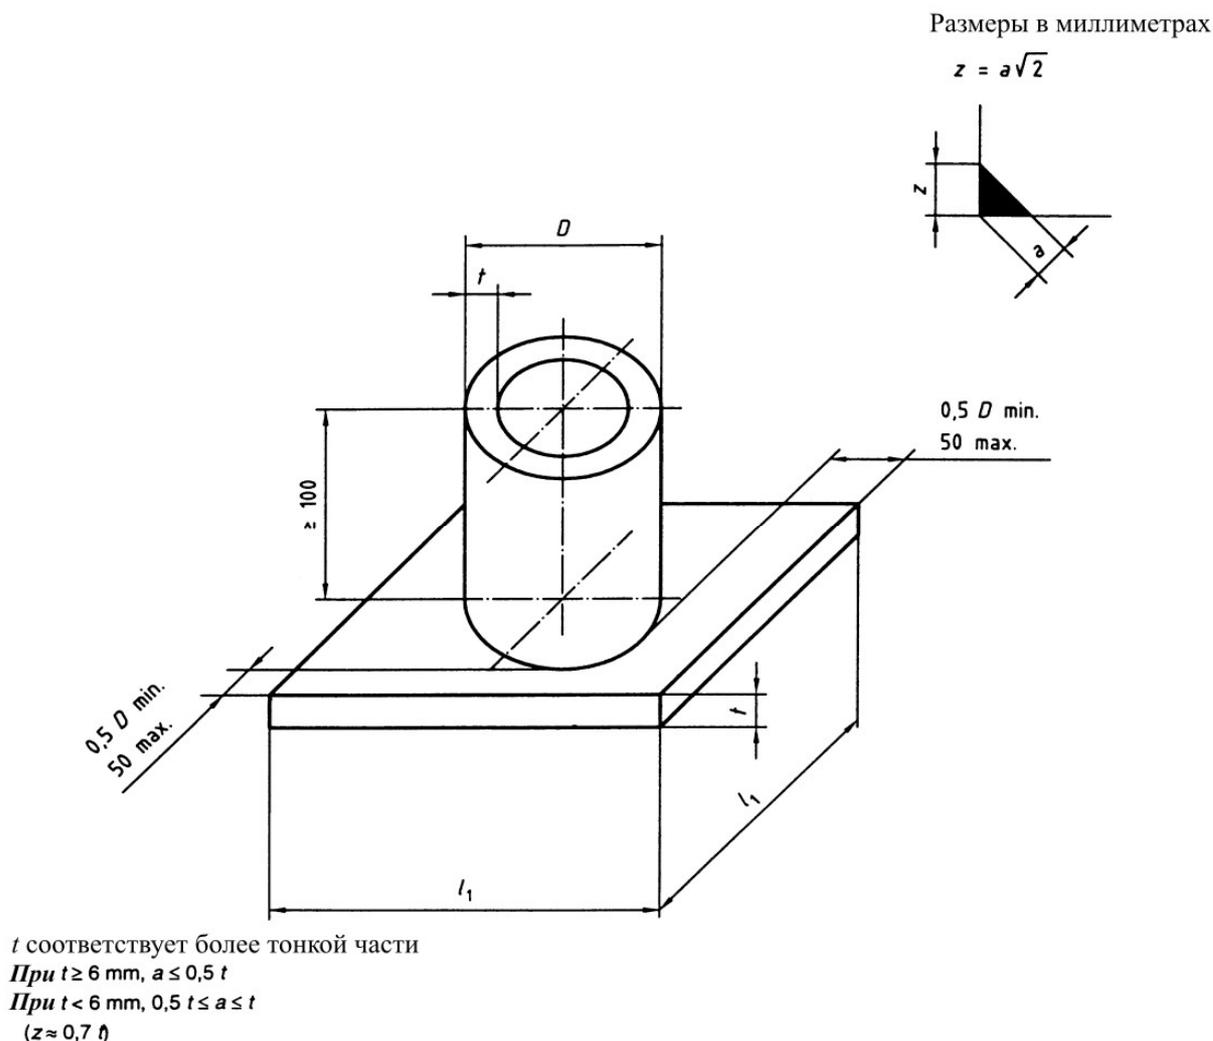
Размеры образца для углового сварного шва в трубе
